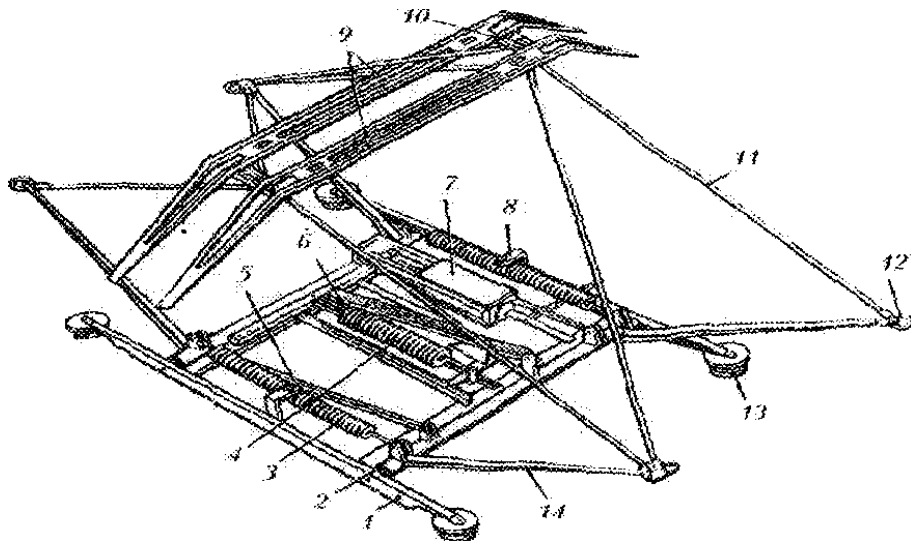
Чотириважільний струмоприймач: 1 - основа на ізоляторах; 2 - два вали нижньої рами; 3 - підйомні пружини; 4 - опускаюча пружина; 5 - пневматичний привод; 6 - тяга; 7 - циліндр; 8 - амортизатори; 9 - полоз; 10 - каретка; 11— верхня трубчата рама; 12 - з'єднувачі; 13 - ізолятори; 14 - труби нижньої рами.
